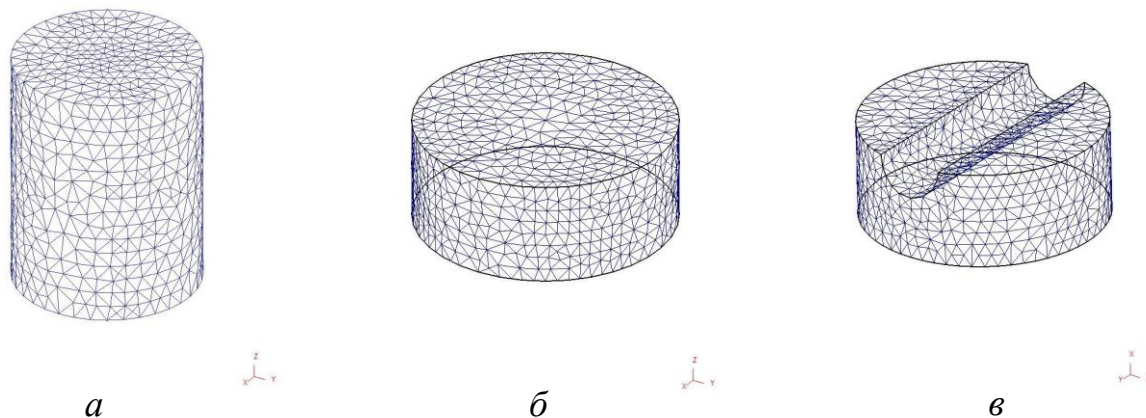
Конечно-элементное разбиение заготовки и бойков:
